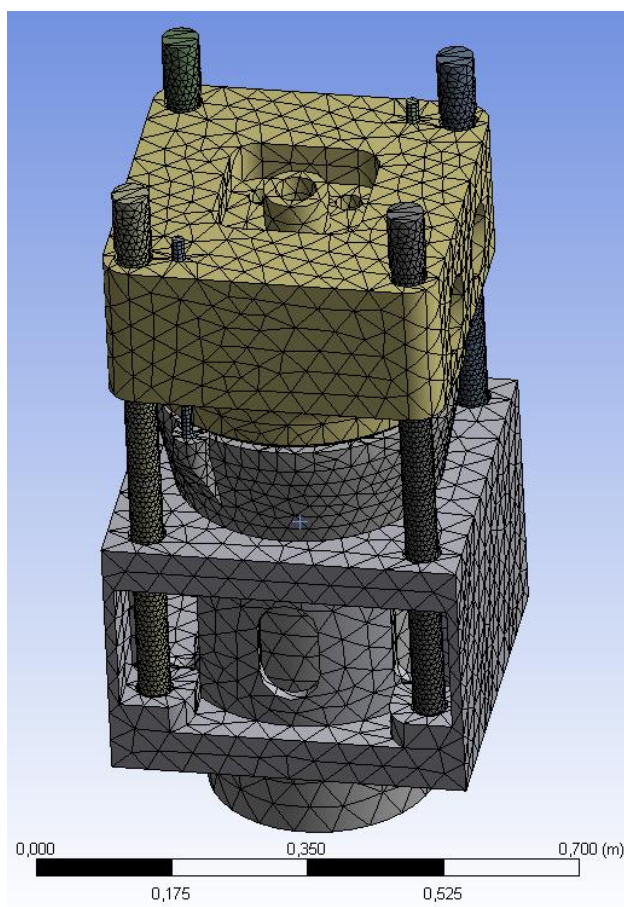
Конечно-элементная модель сборки блока, цилиндра и крышки
